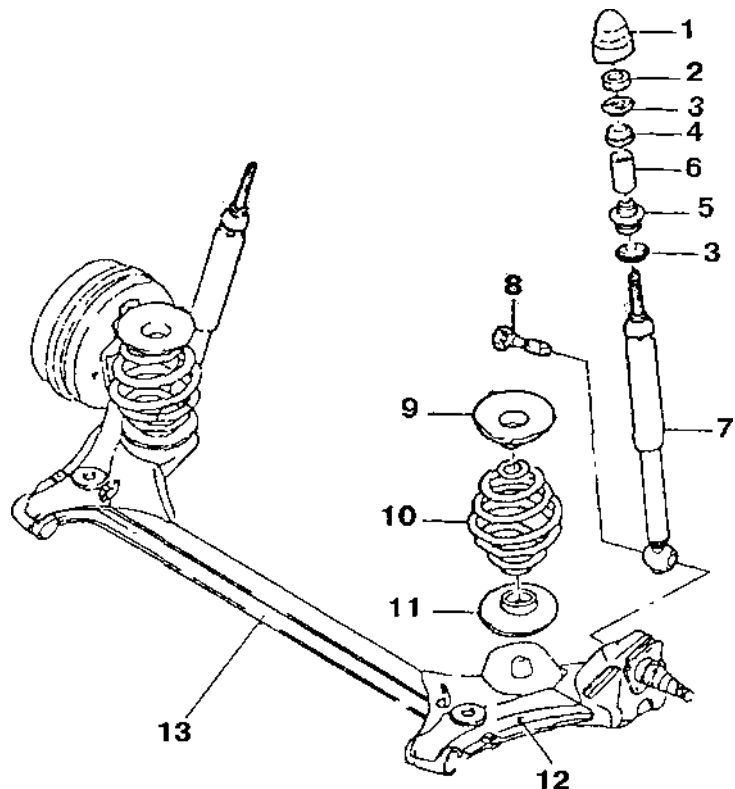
Элементы конструкции упругого, направляющего и гасящего устройств задней подвески:
